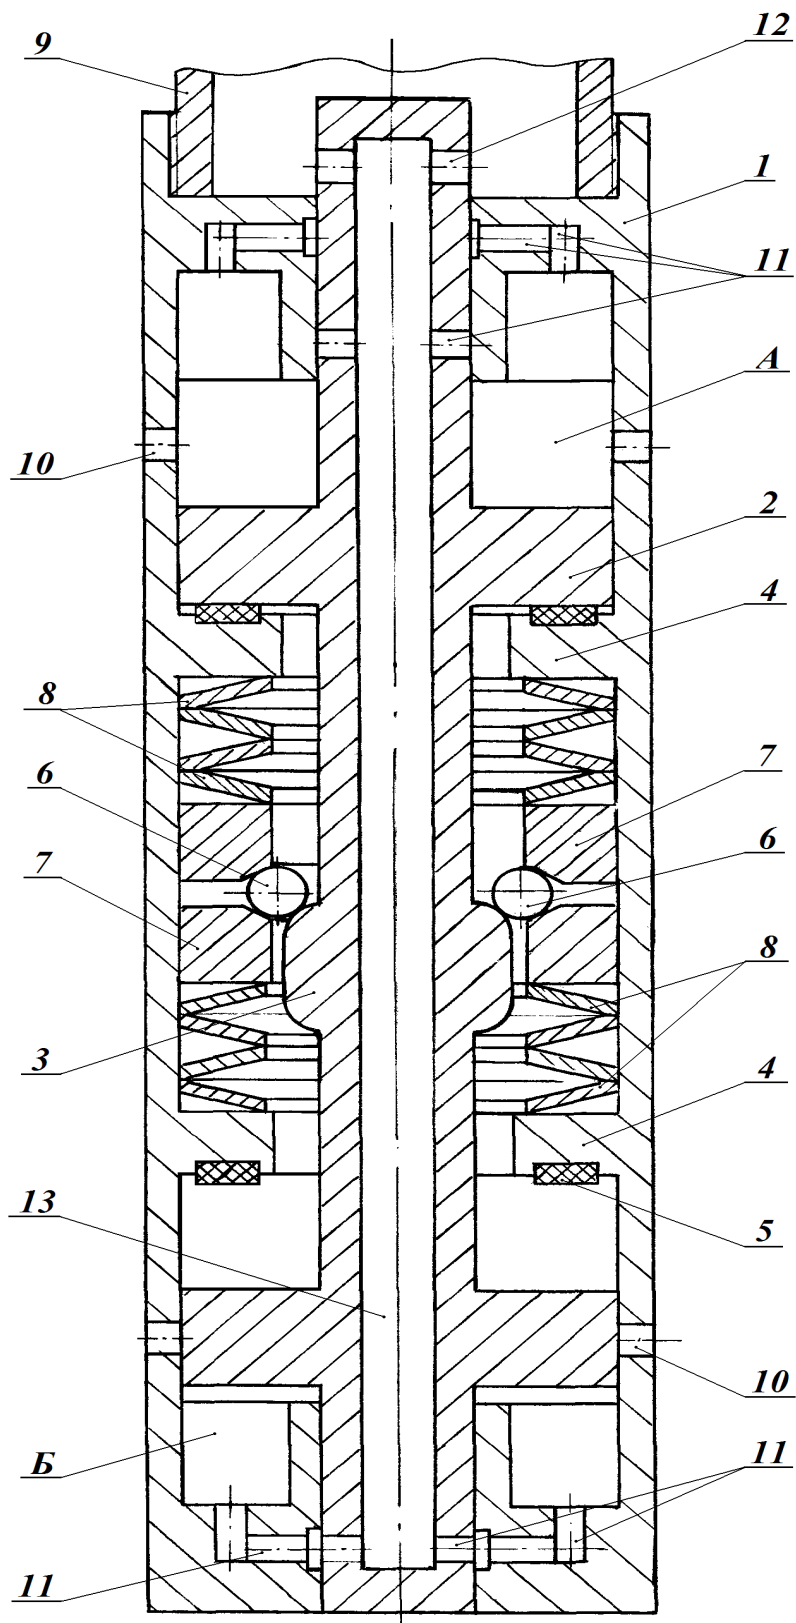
Двухкамерный автоматический пневмопатрон с последовательной разрядкой камер
